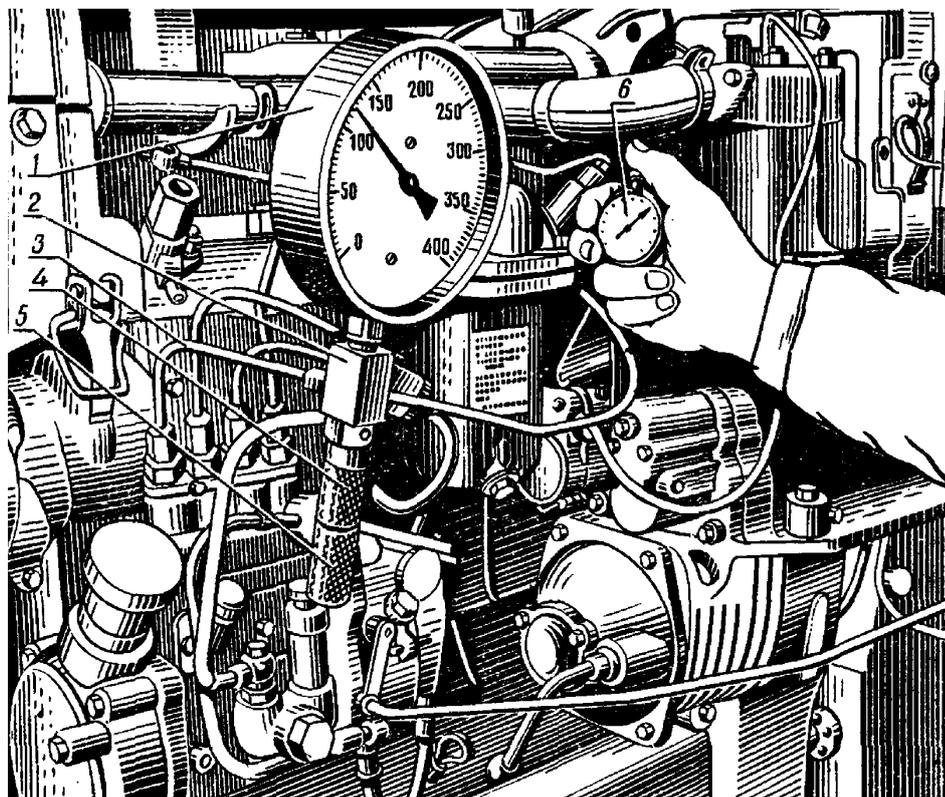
Прибор КИ-4802М: 1 — манометр; 2 — корпус прибора; 3 — топливопровод; 4 — рукоятка; 5 — защитный колпак; 6 — секундомер.
